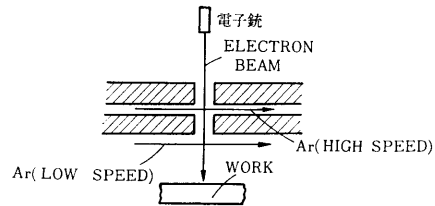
電子ビーム溶接 (SOFT VACUUM TYPE)
